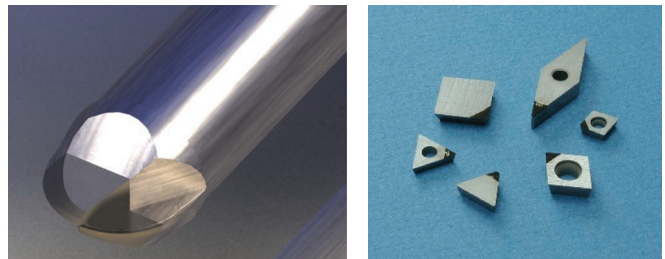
Фреза для высокоскоростного фрезерования с рабочей частью из CVD-алмаза и твердосплавные пластины с вставками из CVD-алмазов.
